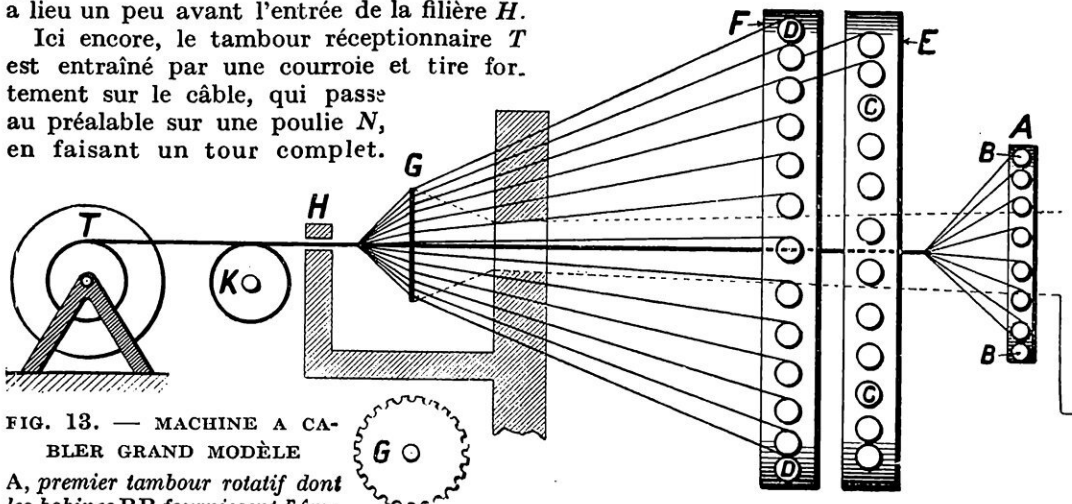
MACHINE A CÂBLER GRAND MODÈLE
